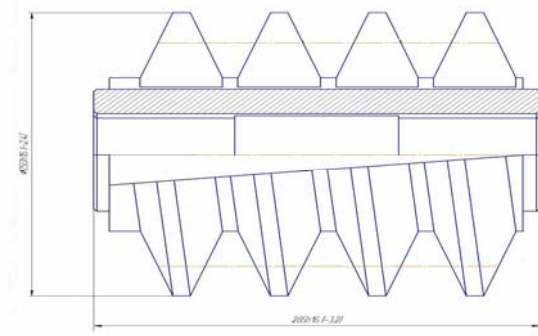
Сварной вариант червячной фрезы модулем 20 мм
